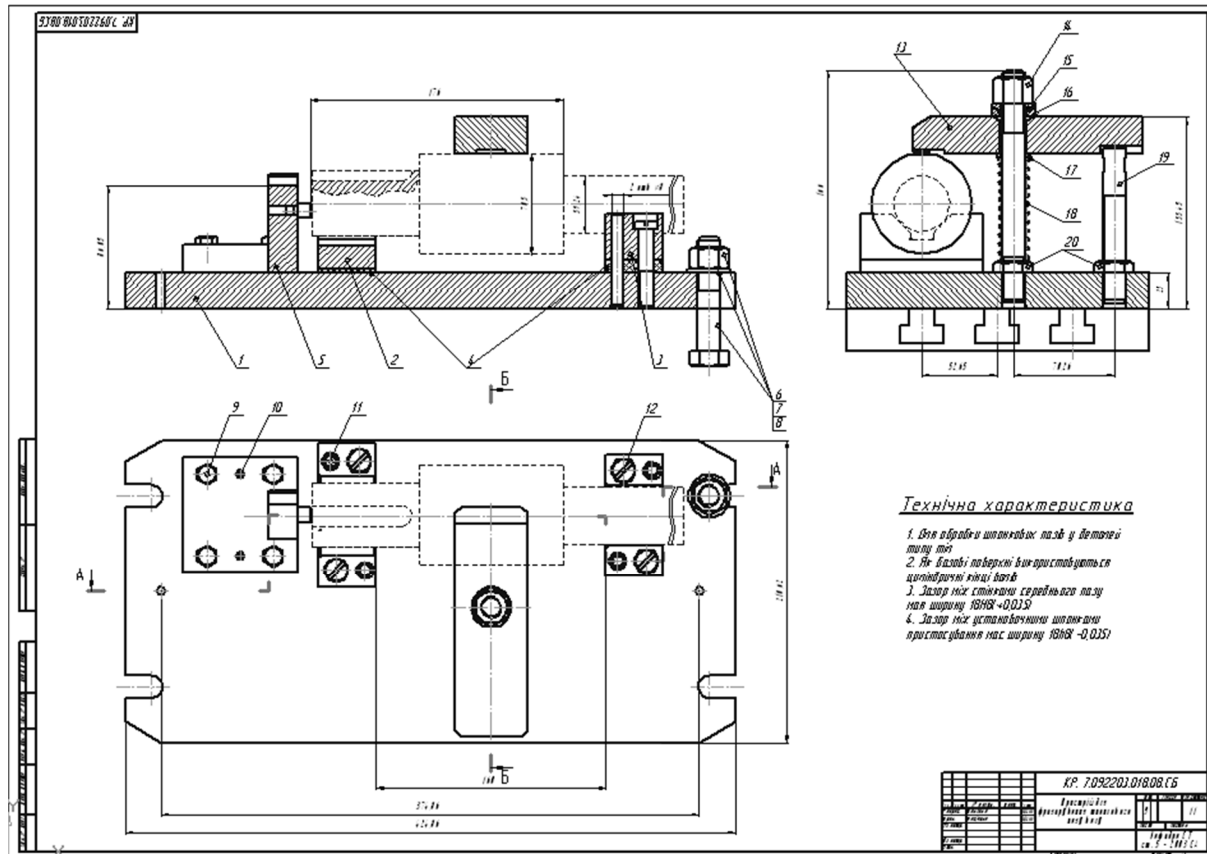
Робоче креслення запроєктованого пристрою
